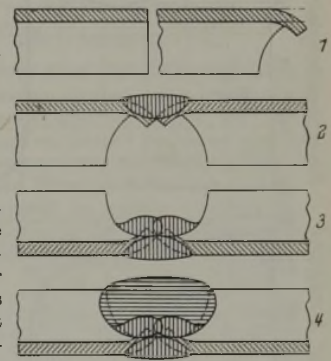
Vorgehen bei der Schweißung von plattiertem Stahl.
